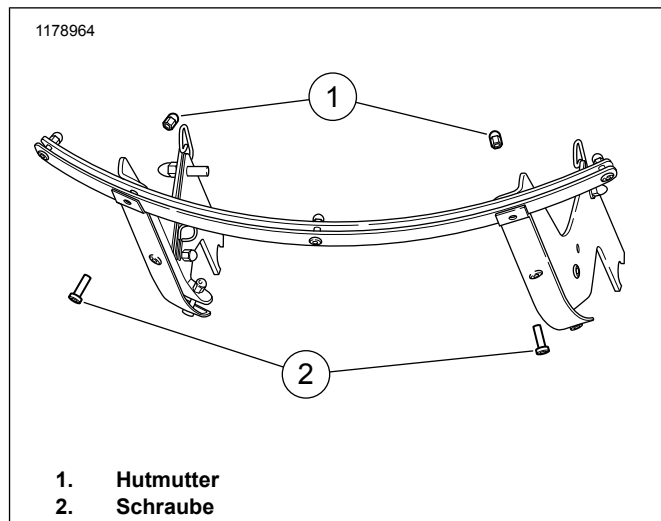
Ausbau der Schraube (Windschutzscheibe zur besseren Sicht ausgebaut)
